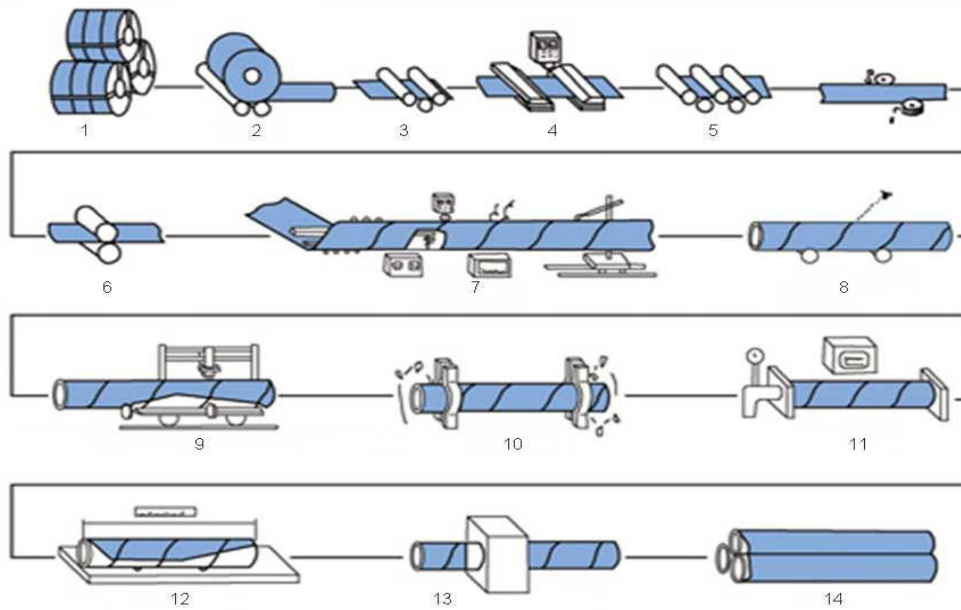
Fabrication des tubes soudés en spirale
